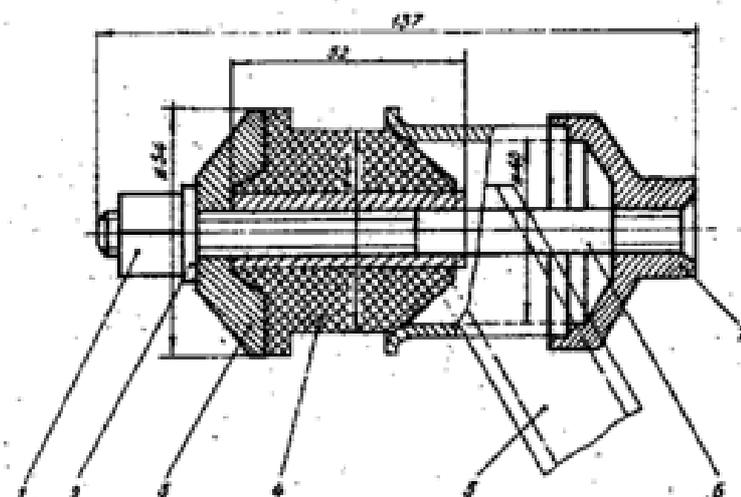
Запрессовка сайлентблока в рычаг балки задней подвески: 1 - гайка; 2 - шайба; 3 - толкатель; 4 - сайлентблок; 5 - рычаг задней подвески; 6 - винт; 7 - опора.
